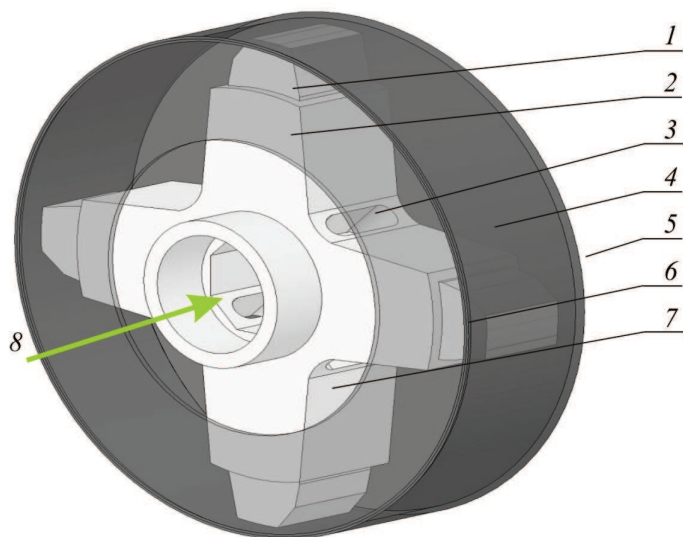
Моделирование процесса внутреннего шлифования: 1 – шлифовальный сегмент; 2 – корпус круга; 3 – отверстие для подачи СОЖ; 4 – обрабатываемая заготовка; 5 – задняя крышка; 6 – передняя крышка; 7 – отверстие для слива СОЖ; 8 – основная подача СОЖ
